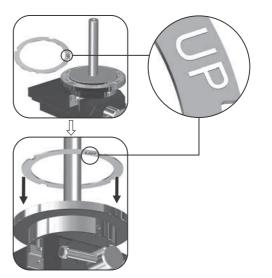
Установка уплотнительного кольца (45) с надписью «UP» (ВВЕРХ), указывающей вниз, в направлении стопора уплотнительного кольца (65)
